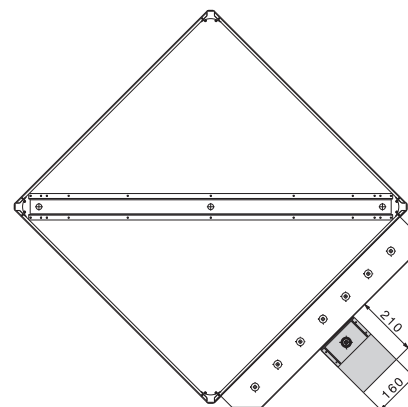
Maßbild Adapter für Ausführung F (in mm)
